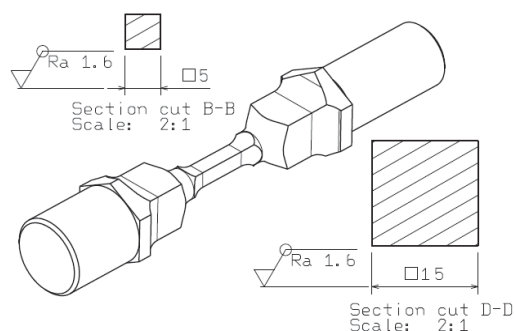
Detail obrobení rozhraní zatěžovacího mechanismu.
